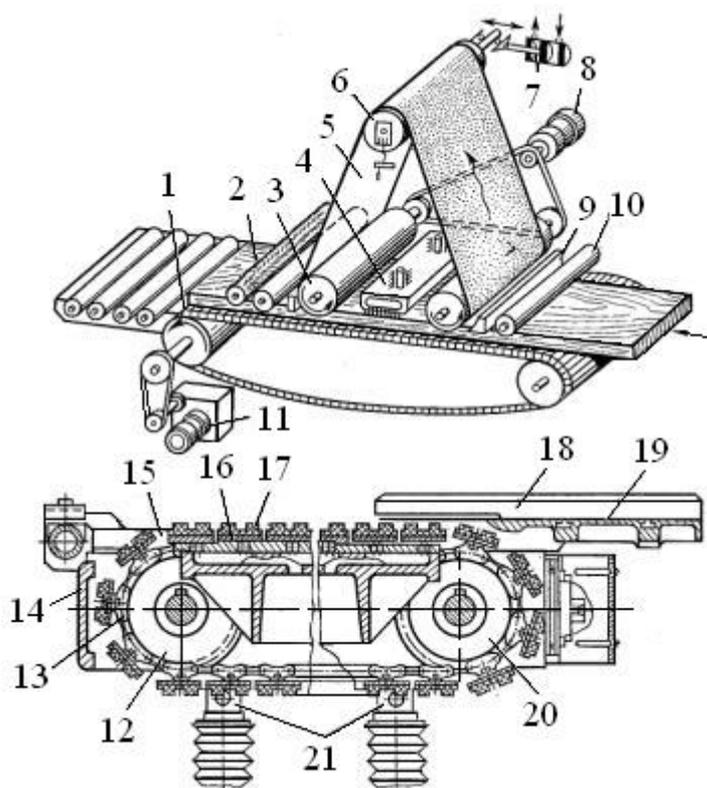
Схема широколенточного станка ШЛК-8 с конвейерным механизмом подачи:
